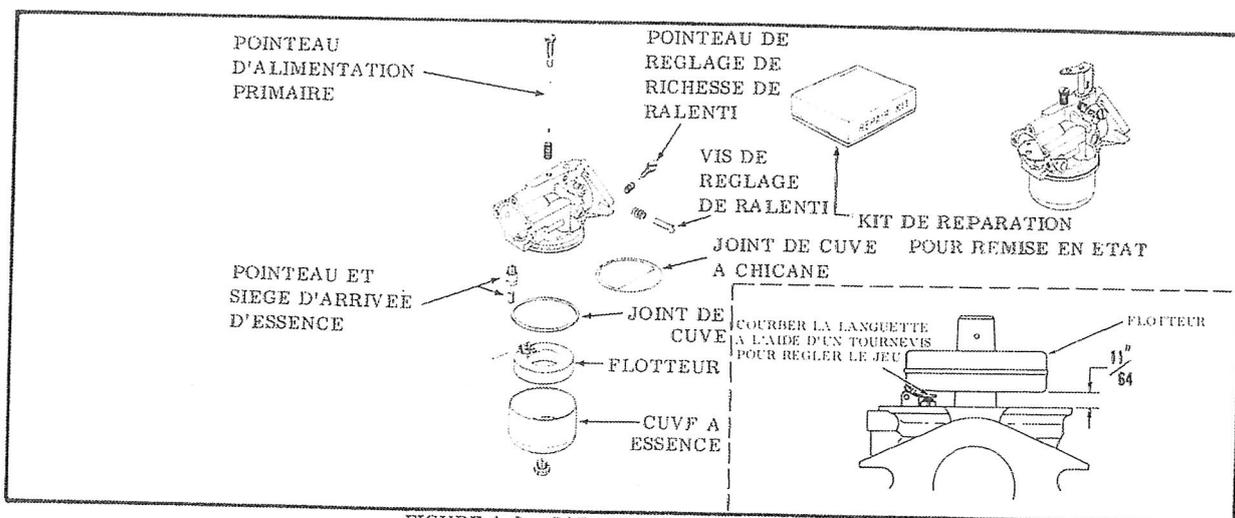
CARBURATEUR HORIZONTAL
